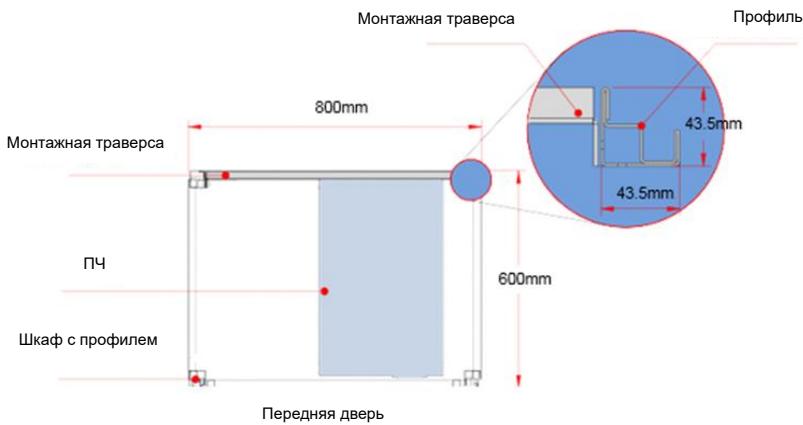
Вид сверху крепления GD270-280-4-GD270-500-4 в шкафу
